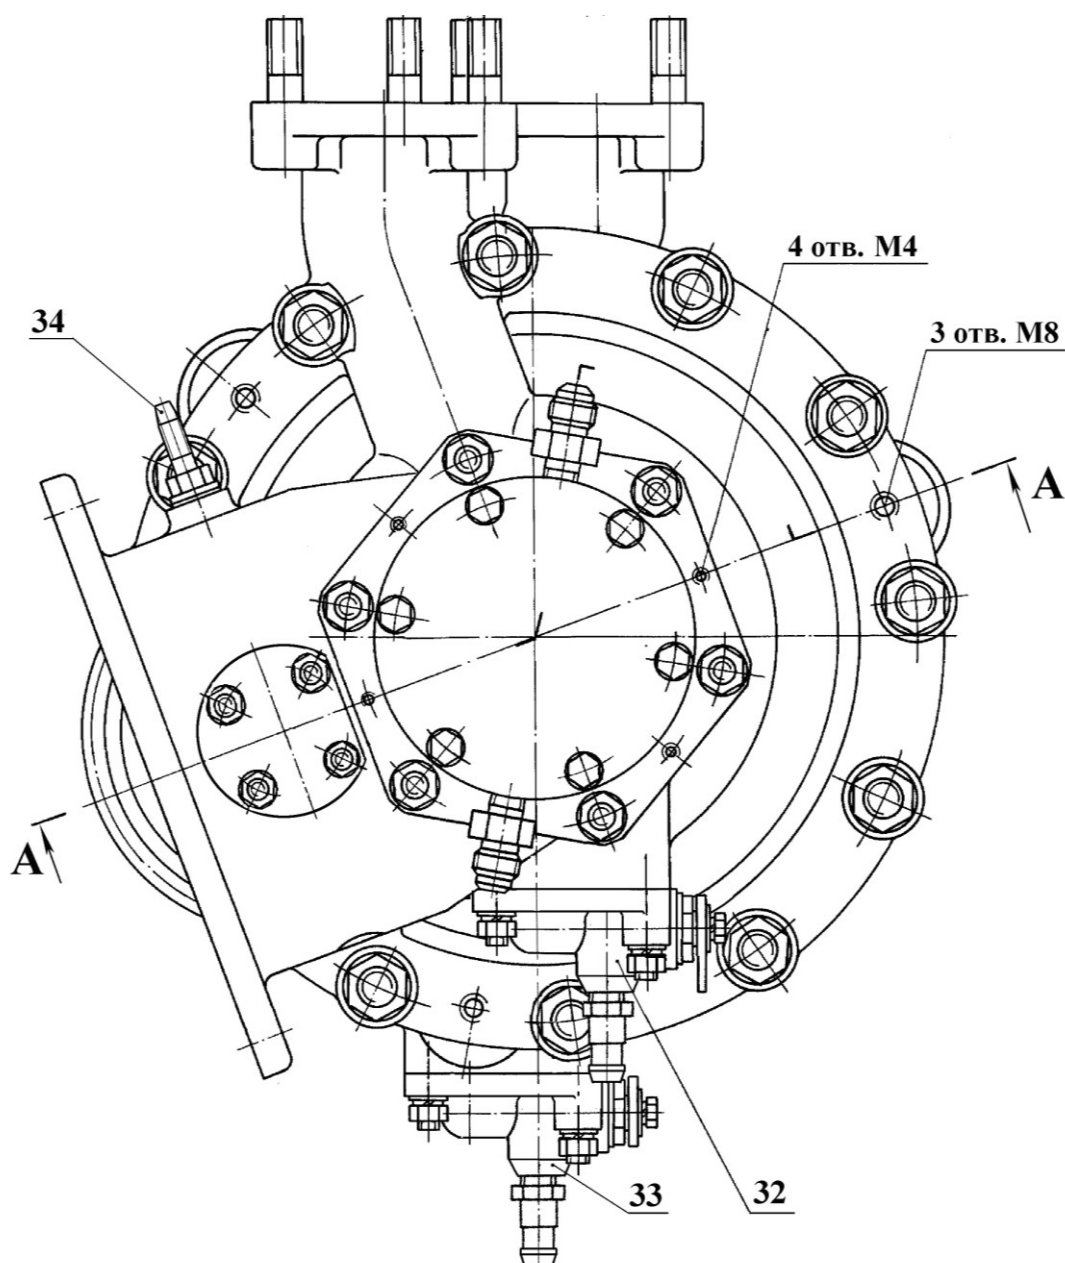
Ступень высокого давления 1 – подшипник; 3 – корпус подшипника; 4 – вал-шестерня; 5 – корпус насоса; 6 – манжета; 7 – винт фиксирующий; 9 – кольцо; 10 – шайба; 11 – гайка корончатая; 12 – шплинт; 13 – втулка; 14 – корпус насоса; 15 – аппарат направляющий; 16 – колесо рабочее с лопатками, закрученными направо (если смотреть со стороны входа в колесо); 17 – аппарат направляющий; 18 – колесо рабочее с лопатками, закрученными налево; 21 – сальниковое уплотнение вала; 22 – кольцо; 23 – колесо зубчатое; 24 – подшипник; 25 – ось; 28 – прокладка регулировочная; 30, 31 – крышка; 32, 33 – кран сливной; 34 – пробка. Кольца уплотнительные по 2, 8, 19, 20, 26, 29
